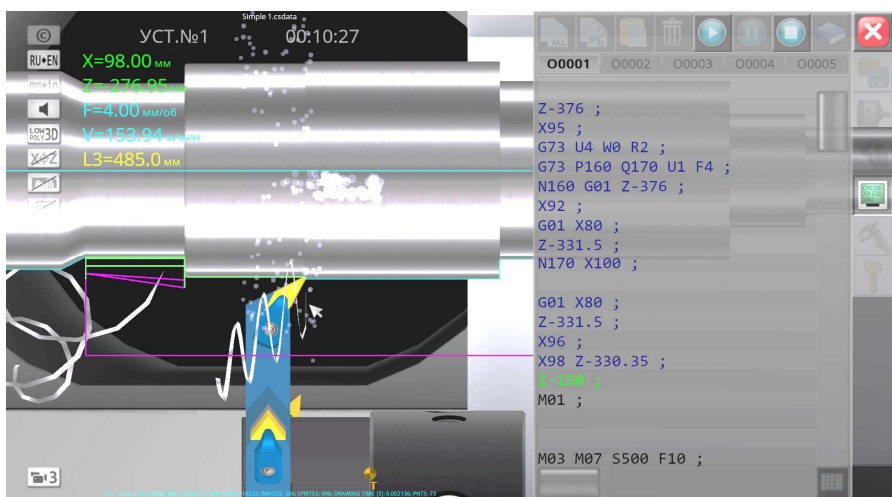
Точение шейки вала Ø80 и фаски 3x45°
